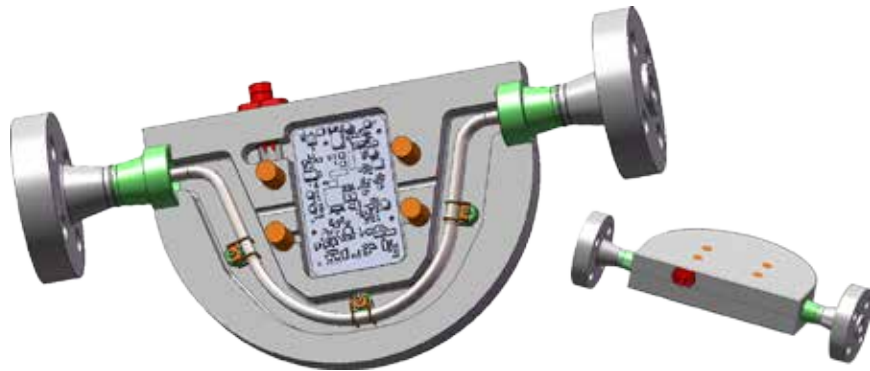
Finales Design mit druckfestem Gehäuse, eingebauter Platine, Sensor, Flanschanschlüssen und Subsea-Steckverbinder.
